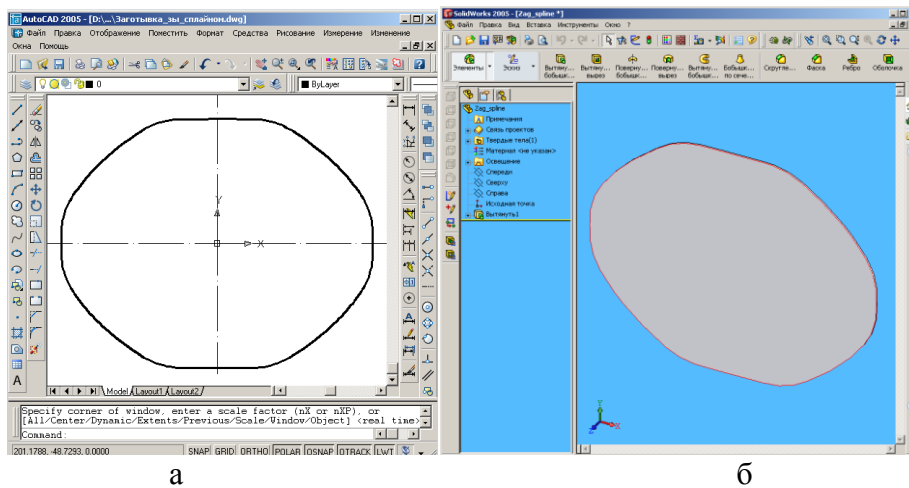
Інструменти, створені у SolidWorks: а– креслення та б – твердотільна модель заготовки для витягування порожнистого коробчастого виробу.
